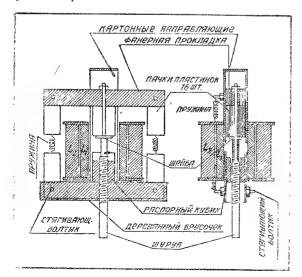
Сборочный чертеж вдвигающегося серлечника и катушек
